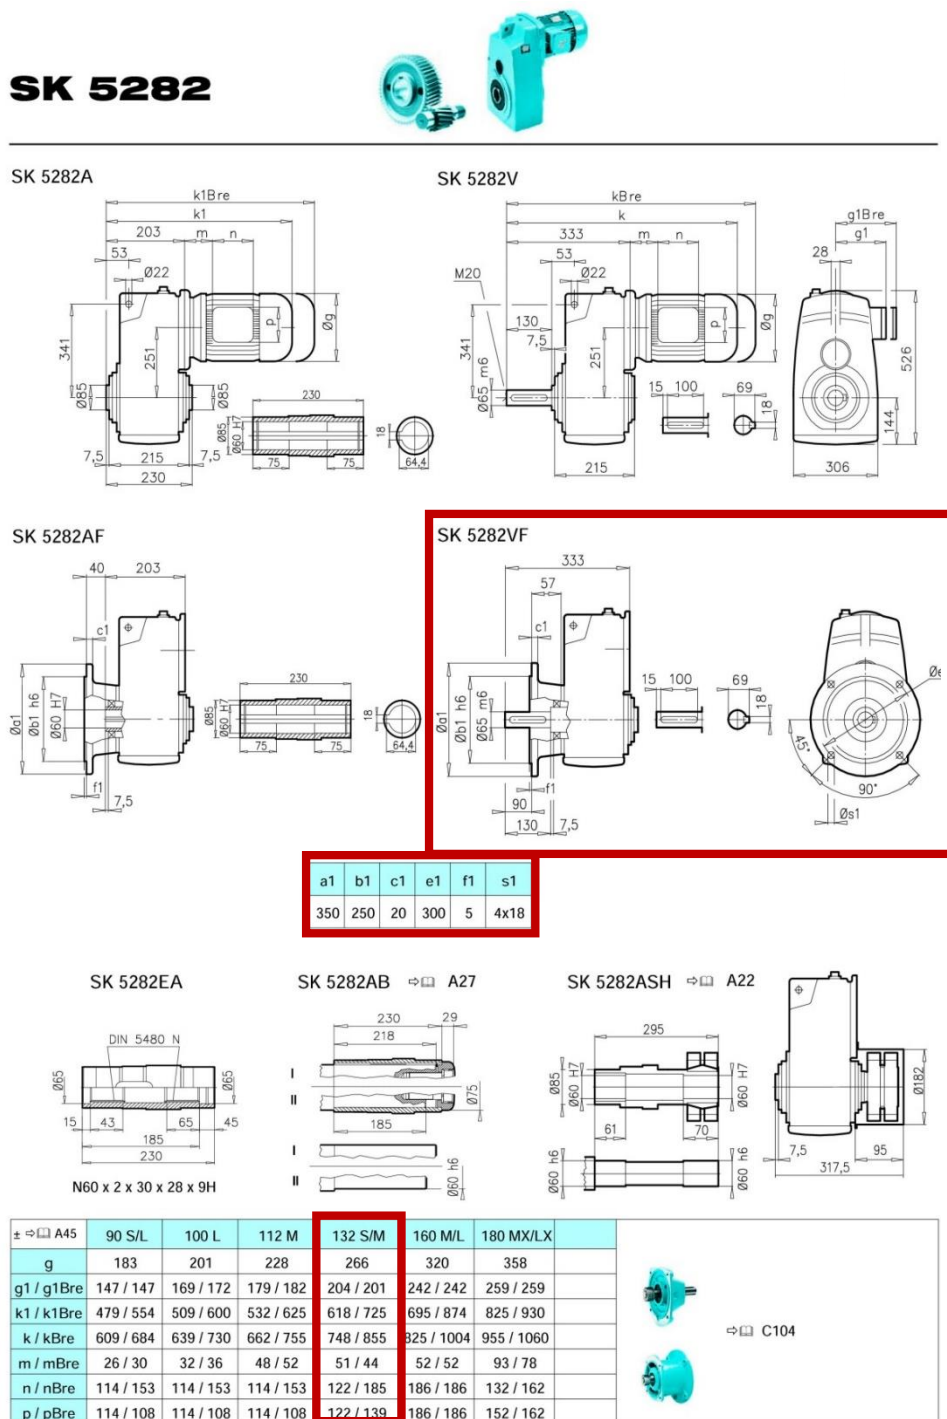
Dimensiones generales del moto-reductor seleccionado
